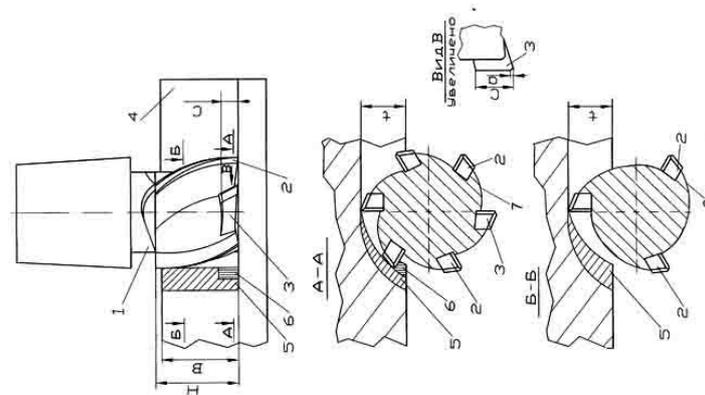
Конструктивная схема концевой фрезы с равной стойкостью торцовых режущих лезвий, в которой у торцовой части имеют затылки и специальные и стандартные зубья.
